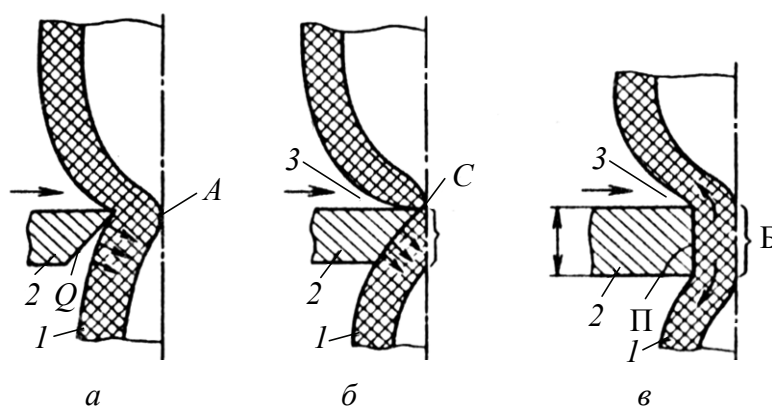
Заготовка в момент начала пережима пресс-кантами
